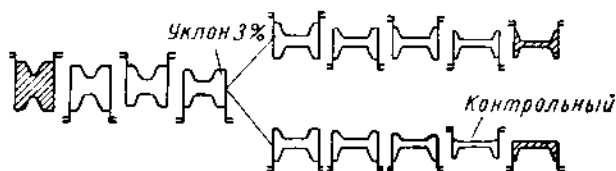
Схема прокатки двутавровых балок и швеллеров
